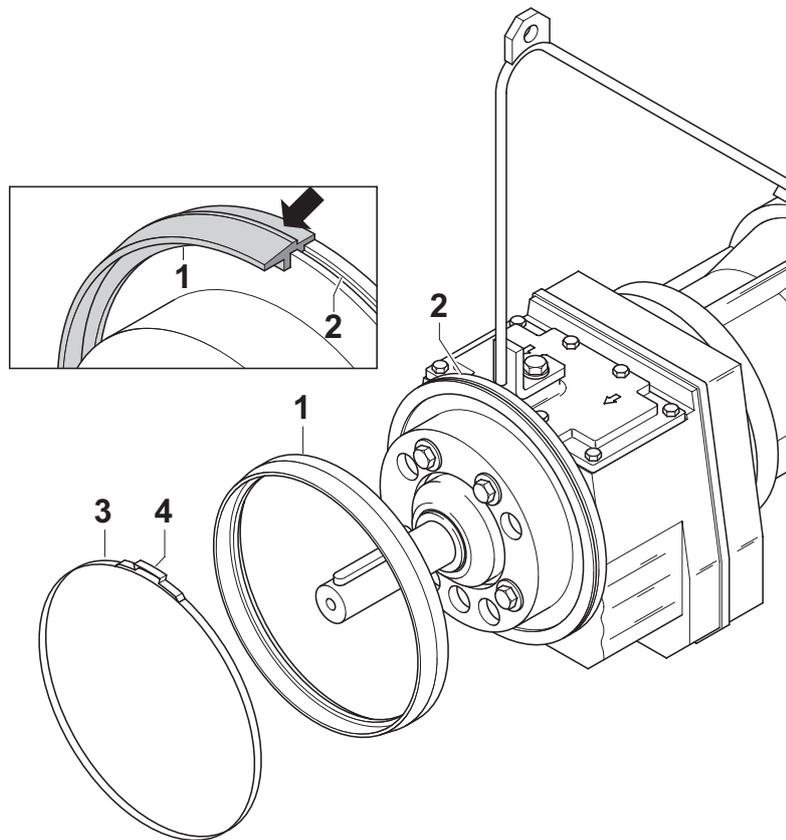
Montagem/Desmontagem do Solids-Deflection-Ring
